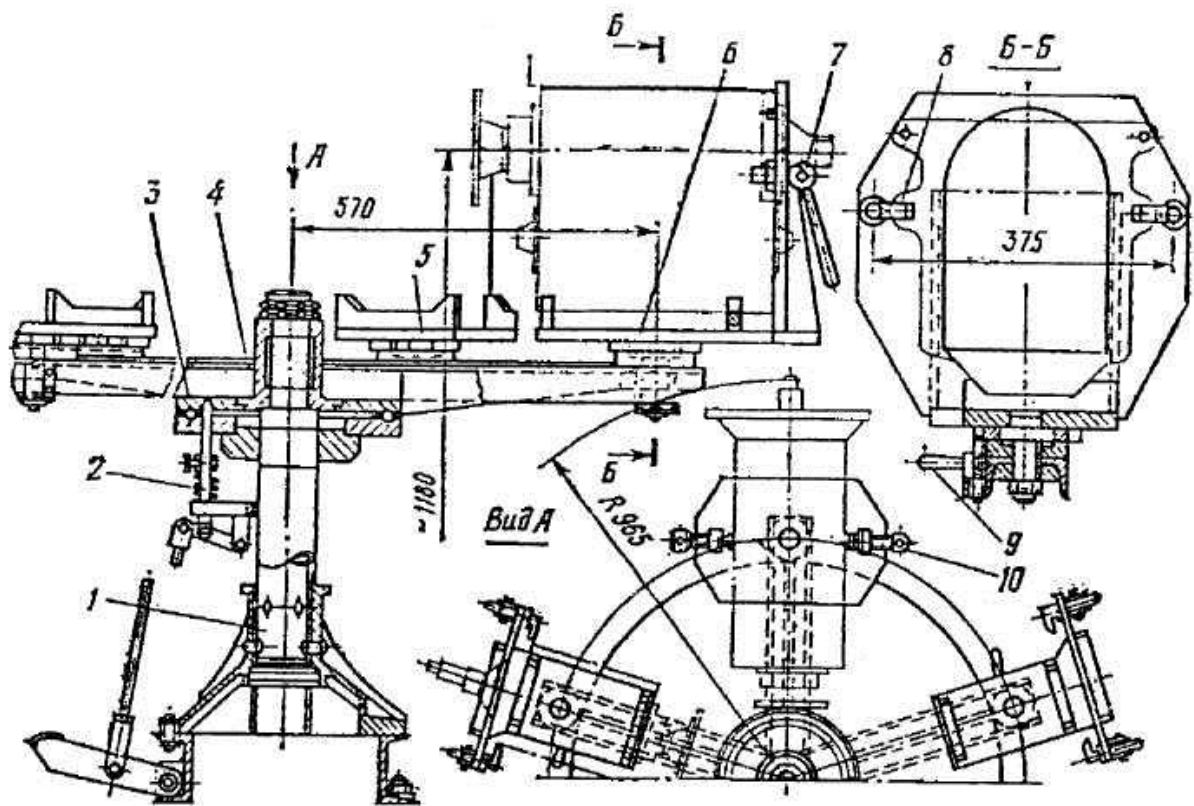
Стенд для розбирання коробки передач, модель 801-9
